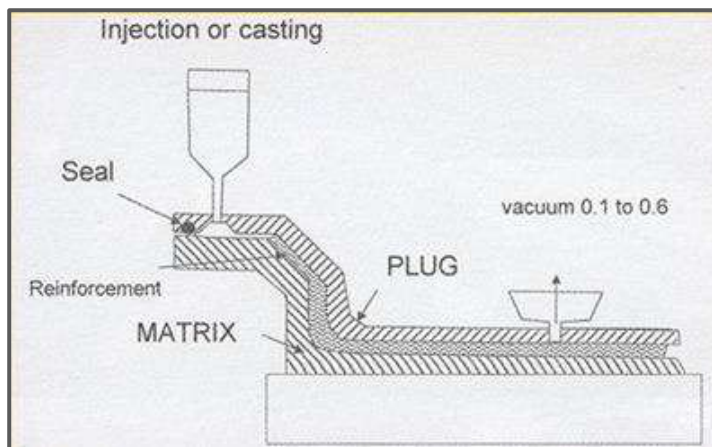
Schema del processo di Vacuum Assisted Resin Transfer Molding
